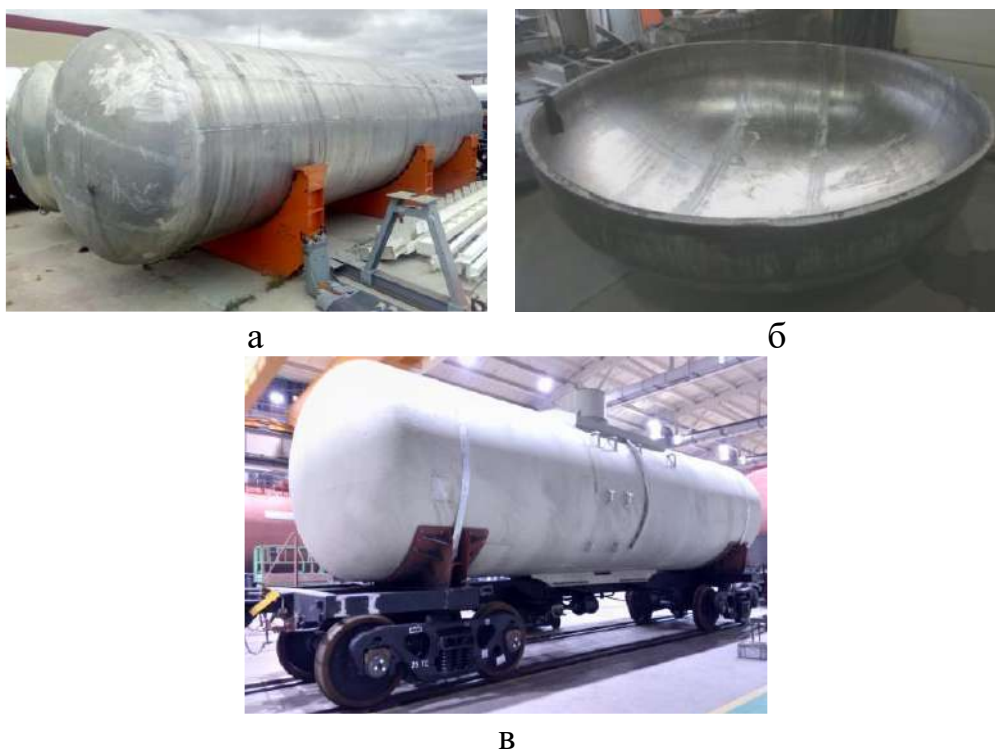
Сварной котел цистерны (а), сварное днище после раскатки (б) и цистерна (в) из сплава АД0 для перевозки азотной кислоты
